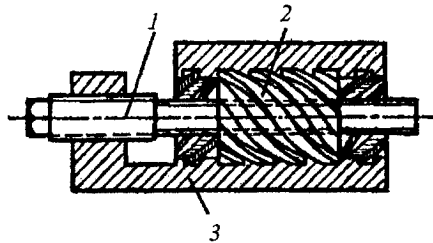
Триланковий гвинтовий механізм: 1,2 – гвинти, 3 – гайка
